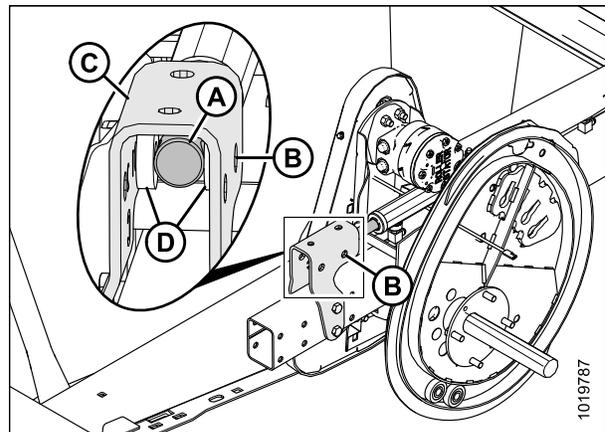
Центральный рычаг подбирающего мотовила
